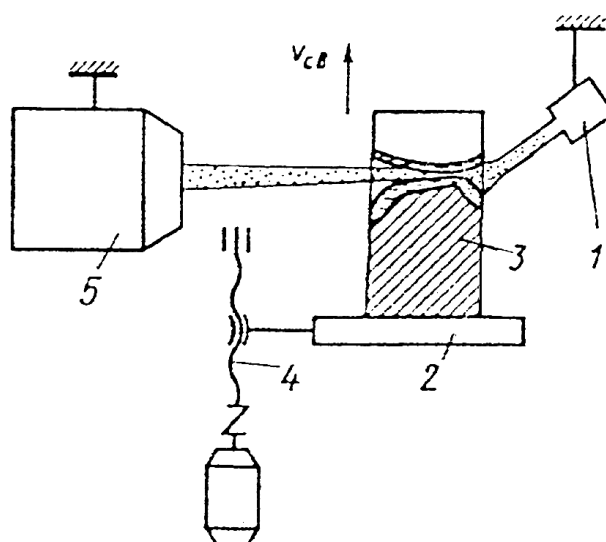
Схема двусторонней электронно-лучевой и дуговой сварки:
